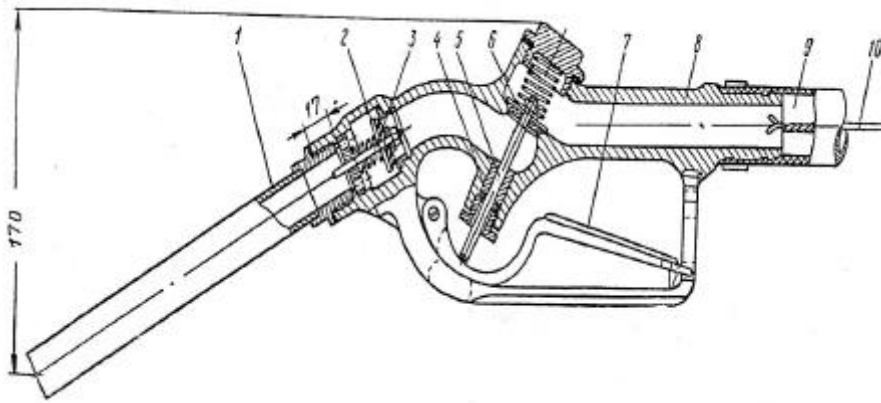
Розріз роздаткового крана: 1 - зливна труба; 2 - гайка отсечного клапана; 3 - отсечной клапан; 4 - сальник; 5 - шток; 6 - клапан з пружиною; 7 - важіль; 8 - корпус; 9 - рукав; 10 - дріт заземлення
